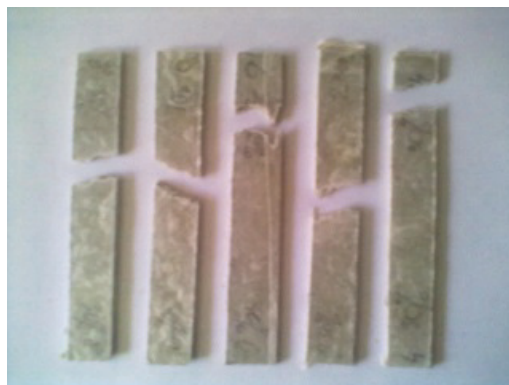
Вид хрупкого разрушения образцов из вторичного пресс-материала
